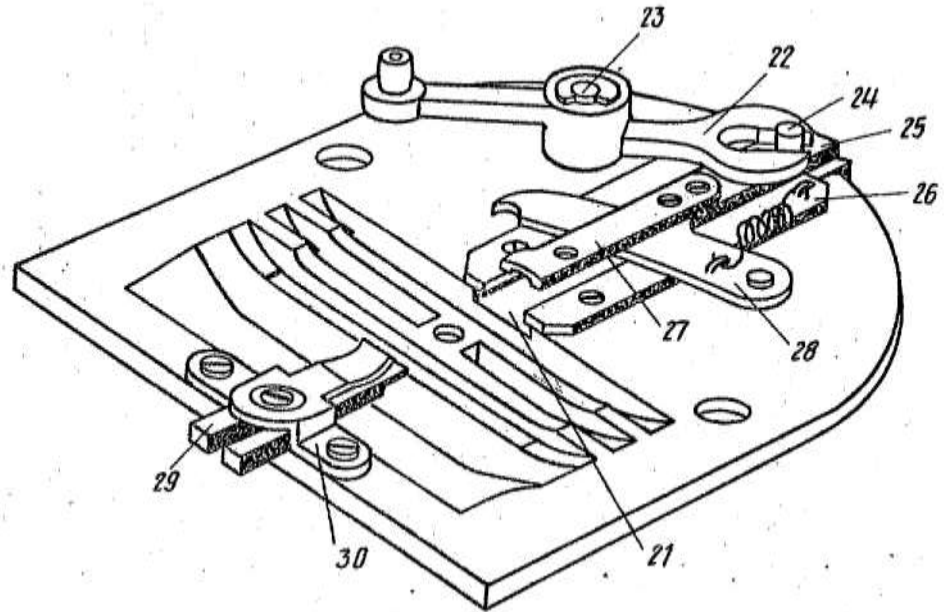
Ножовий пристрій для обрізки ниток, в аксонометрії
